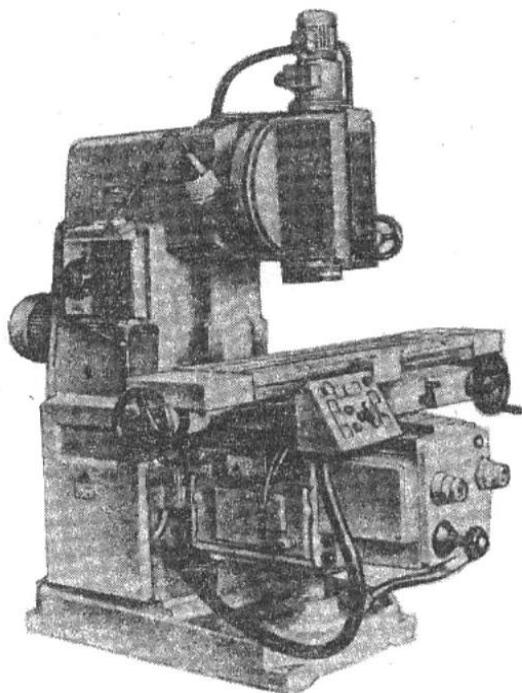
Вертикальный консольно-фрезерный станок 6Т12
